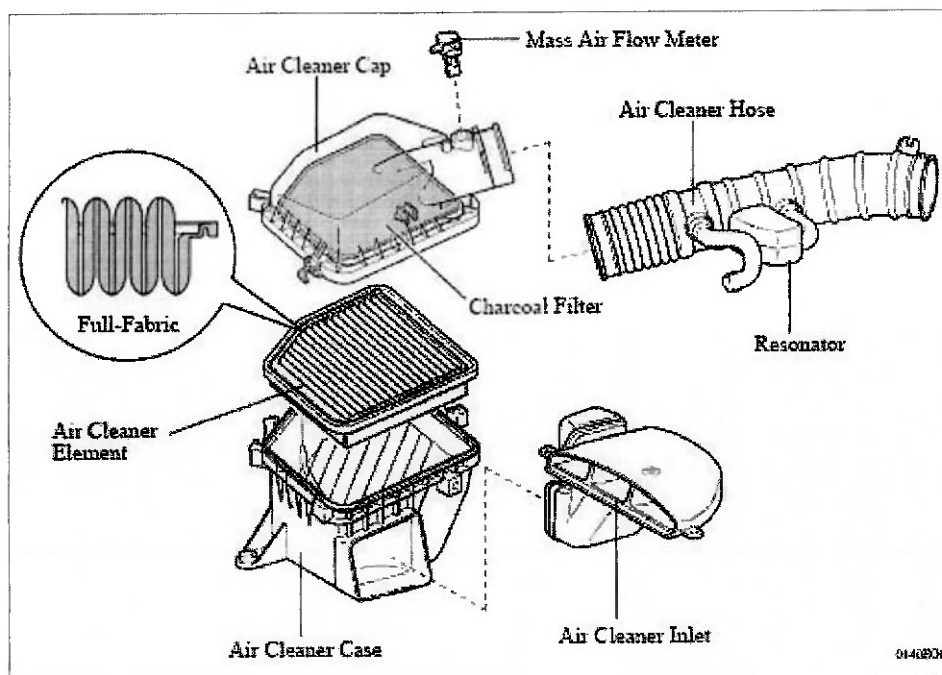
componentes básicos que compõe um sistema de filtração de ar sujo para um motor a combustão interna.
